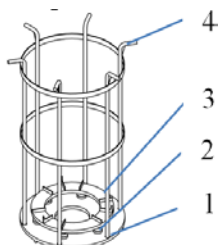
Оснастка для загрузки деталей: 1 – нижняя плита; 2 – изоляторы опорные; 3 – верхняя плита; 4 – стяжки
